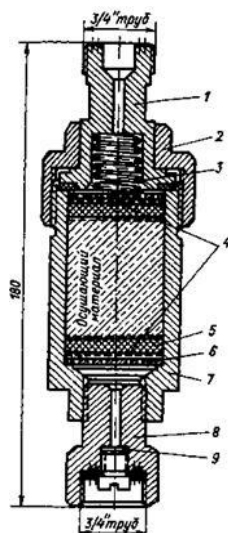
Предредукторный осушитель: 1 – втулка, 2 – гайка, 3 – пружина, 4 – сетчатые шайбы, 5 – фильтры из стекловаты, 6 – осушитель, 7 – корпус, 8 – втулка, 9 – шайба.
